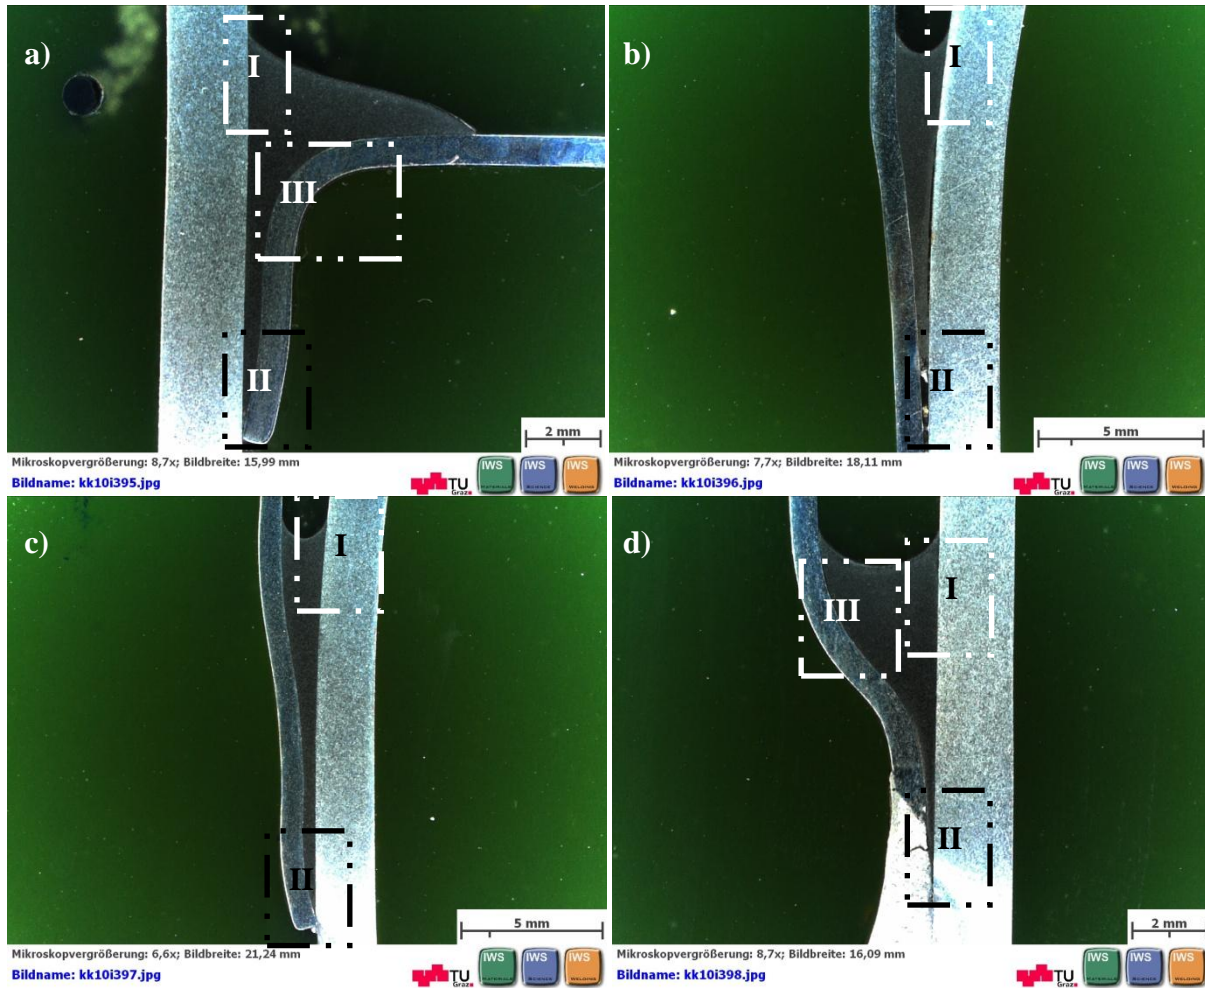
Delta Kompressor Probe 6: a) Pos. A; b) Pos. B; c) Pos. C; d) Pos. D
